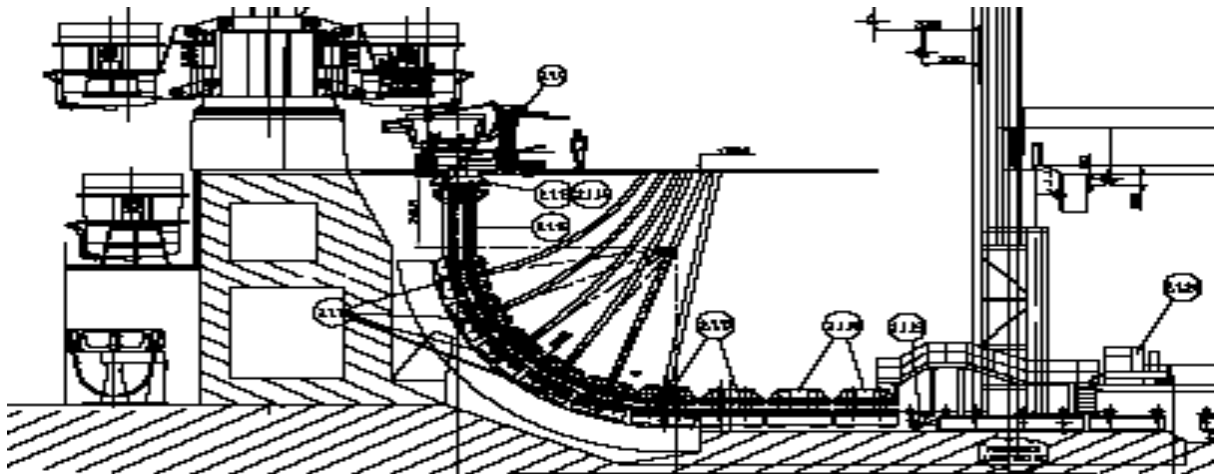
Устройство для приема стальной ковша и поворотный стенд
